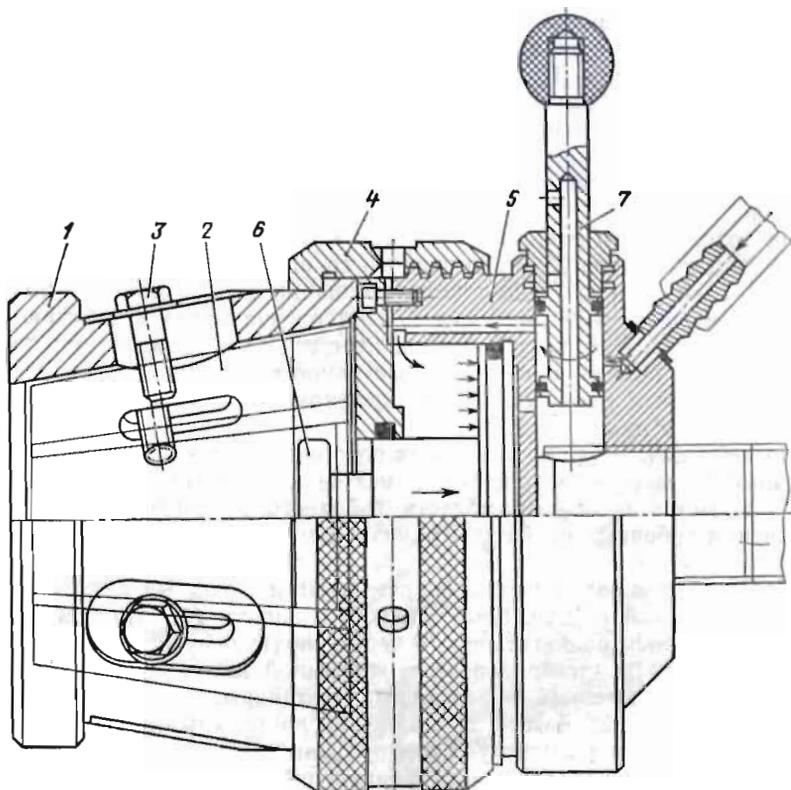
Зажимной патрон профилирующего растяжного станка — конструктивная схема
